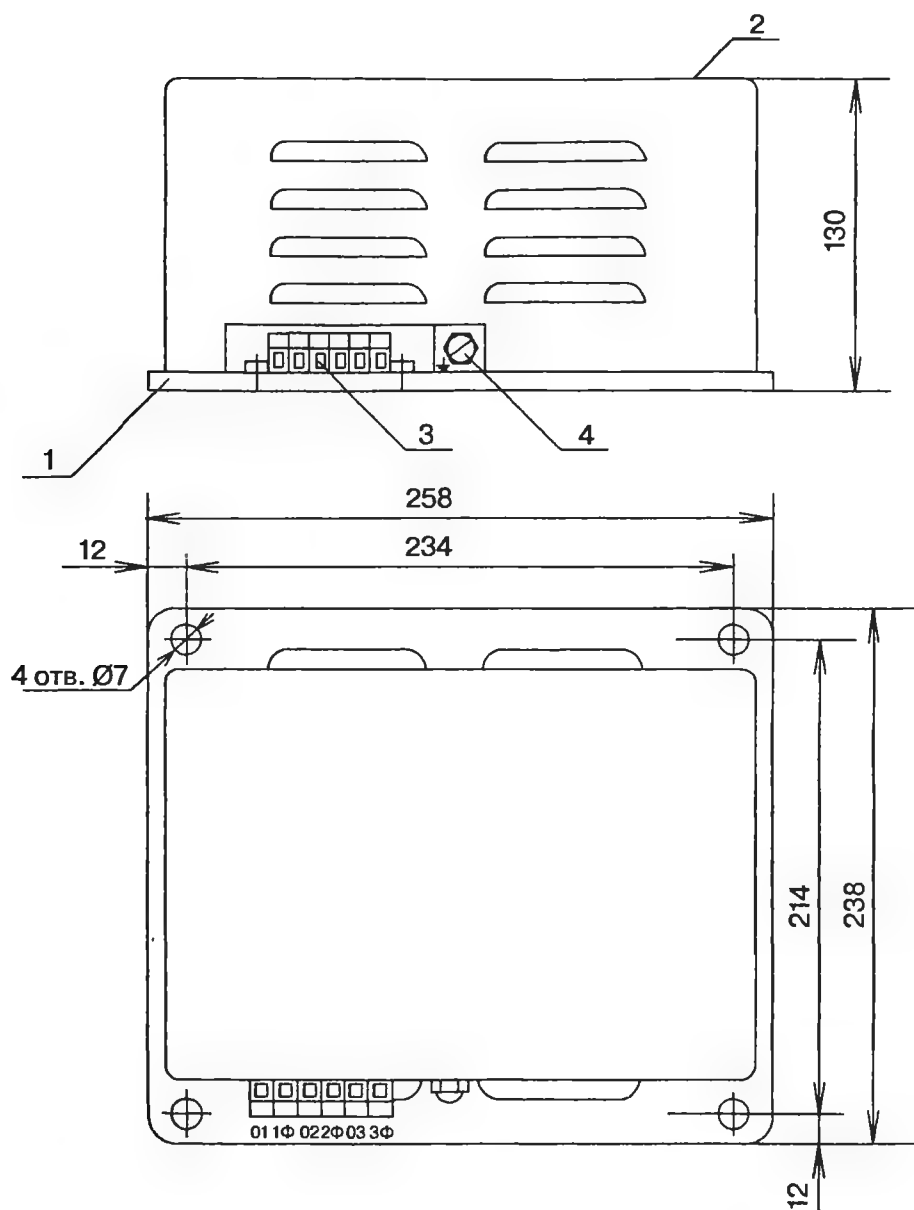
Внешний вид блока БЗПЗ-25 и БЗПЗ-100, где: 1 — основание; 2 — кожух; 3 — клеммной соединитель; 4 — винт заземления
